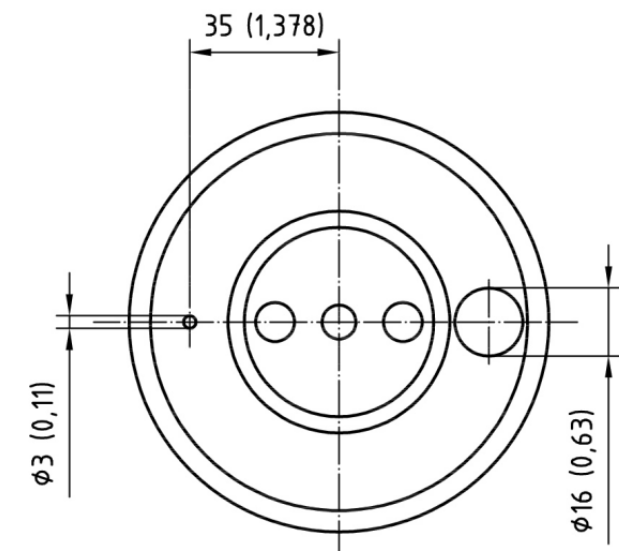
Типовая сборка пресс-формы (вид сверху)
